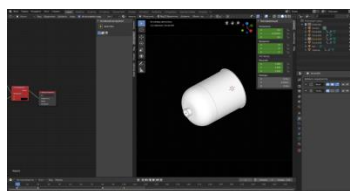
Сборка фрагментов сварной конструкции «Разъемный сосуд»
